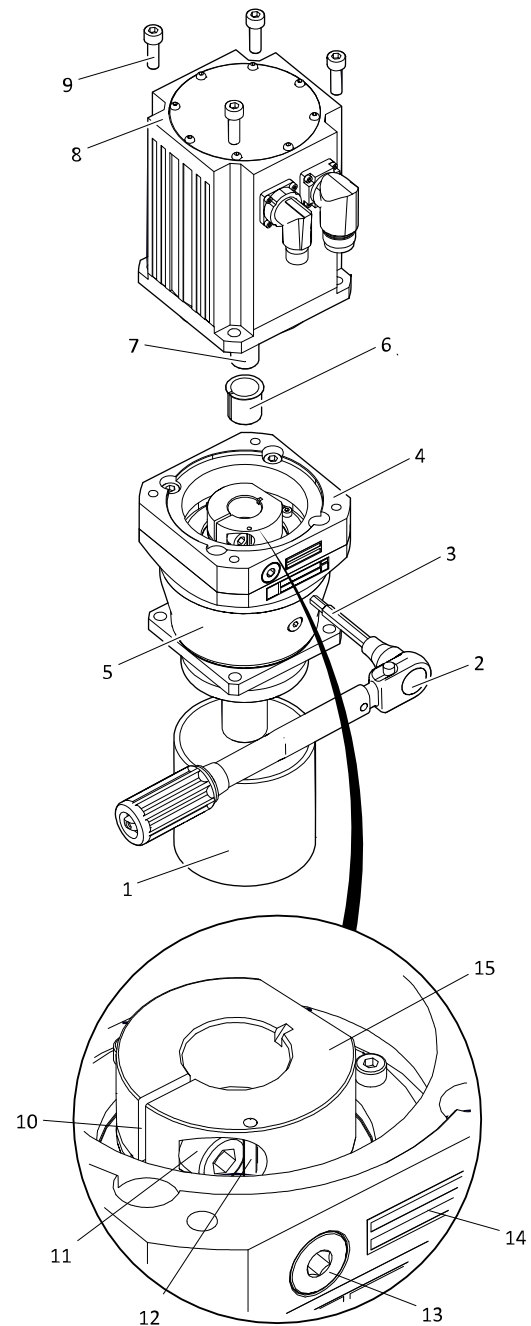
Montage eines Motors an das Planetengetriebe P mit Motoradapter ME (Beispiel)
